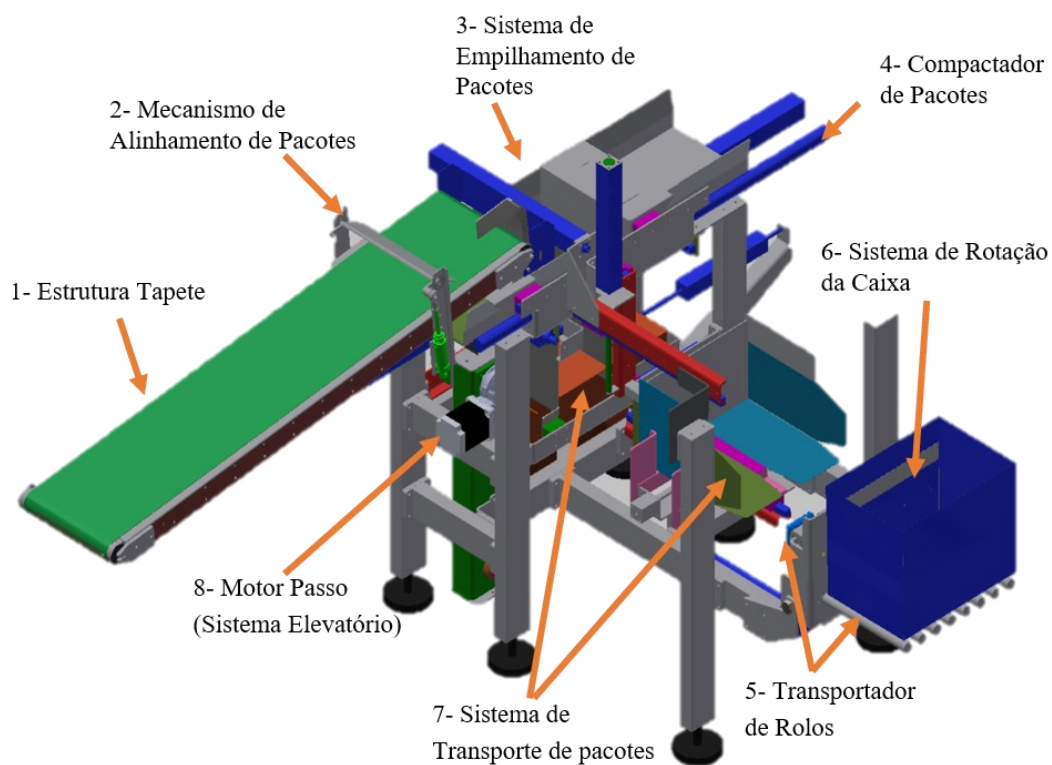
Sistema de enchimento vista 2 CAD 3D
